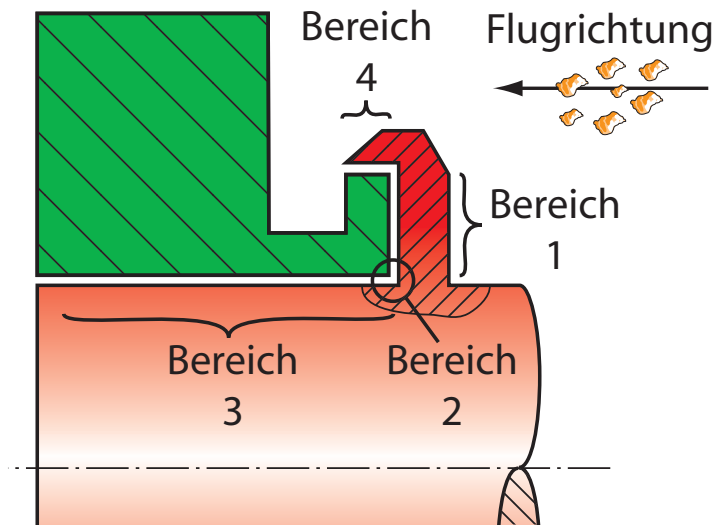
Bereiche im Dichtspalt mit überdecktem Stirnflächenspalt
